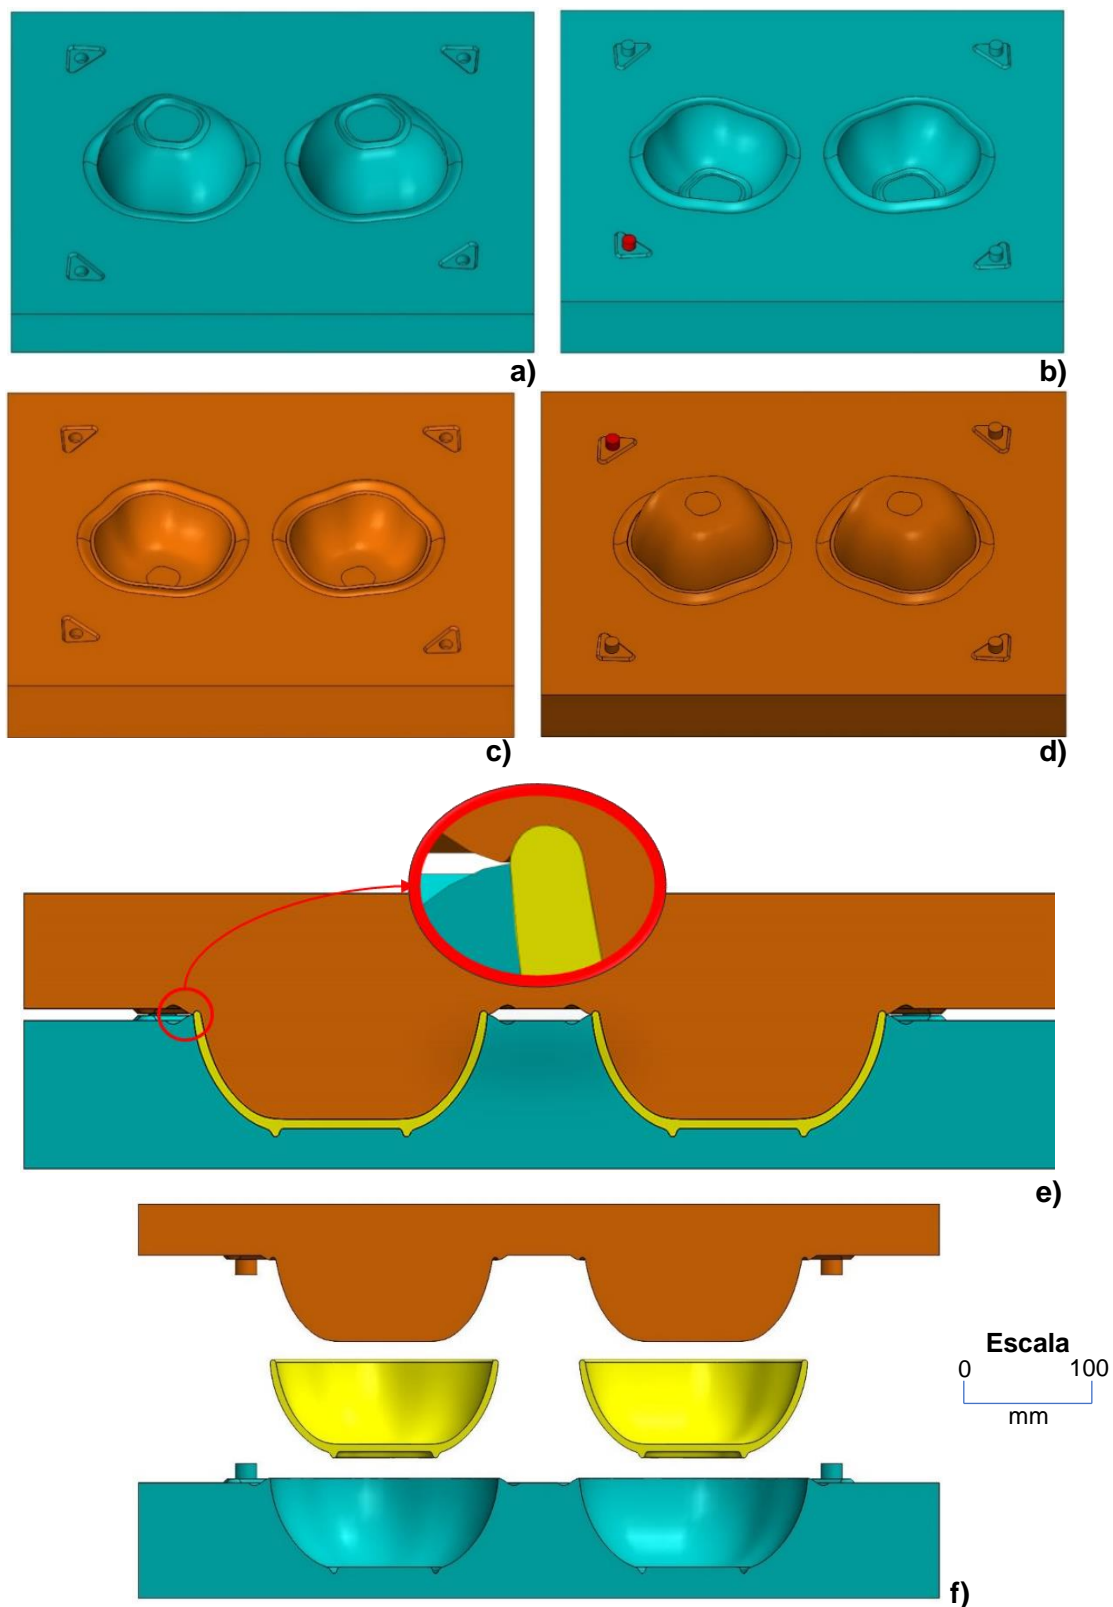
Componentes necessários para a conformação por prensagem RAM da tigela Natura 16: a) e c) madres; b) e d) moldes; e) e f) montagem CAD dos moldes e da tigela.
